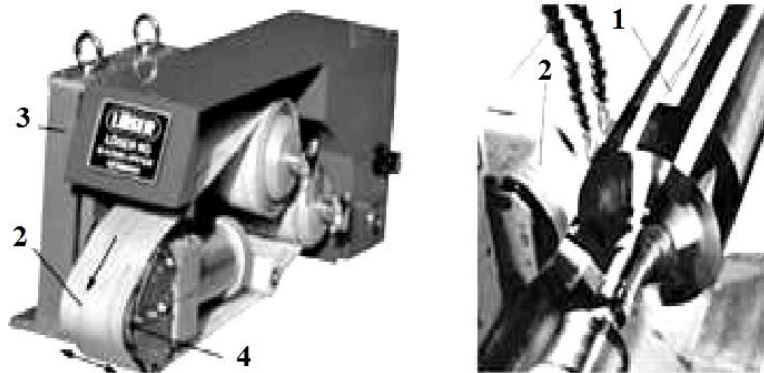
Установка (а) і процес стрічкового суперфінішування (б):
